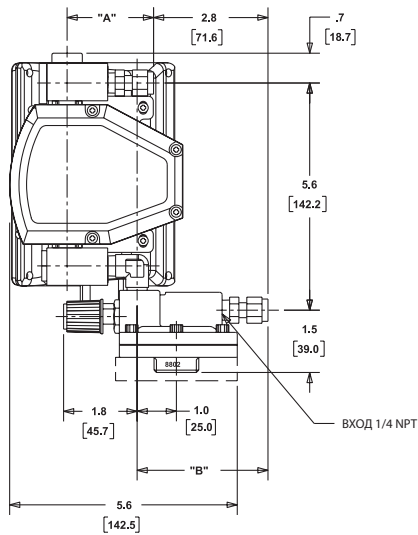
Размеры для резьбовых соединений MT3750C с передатчиком или индуктивным выключателем предельных значений
